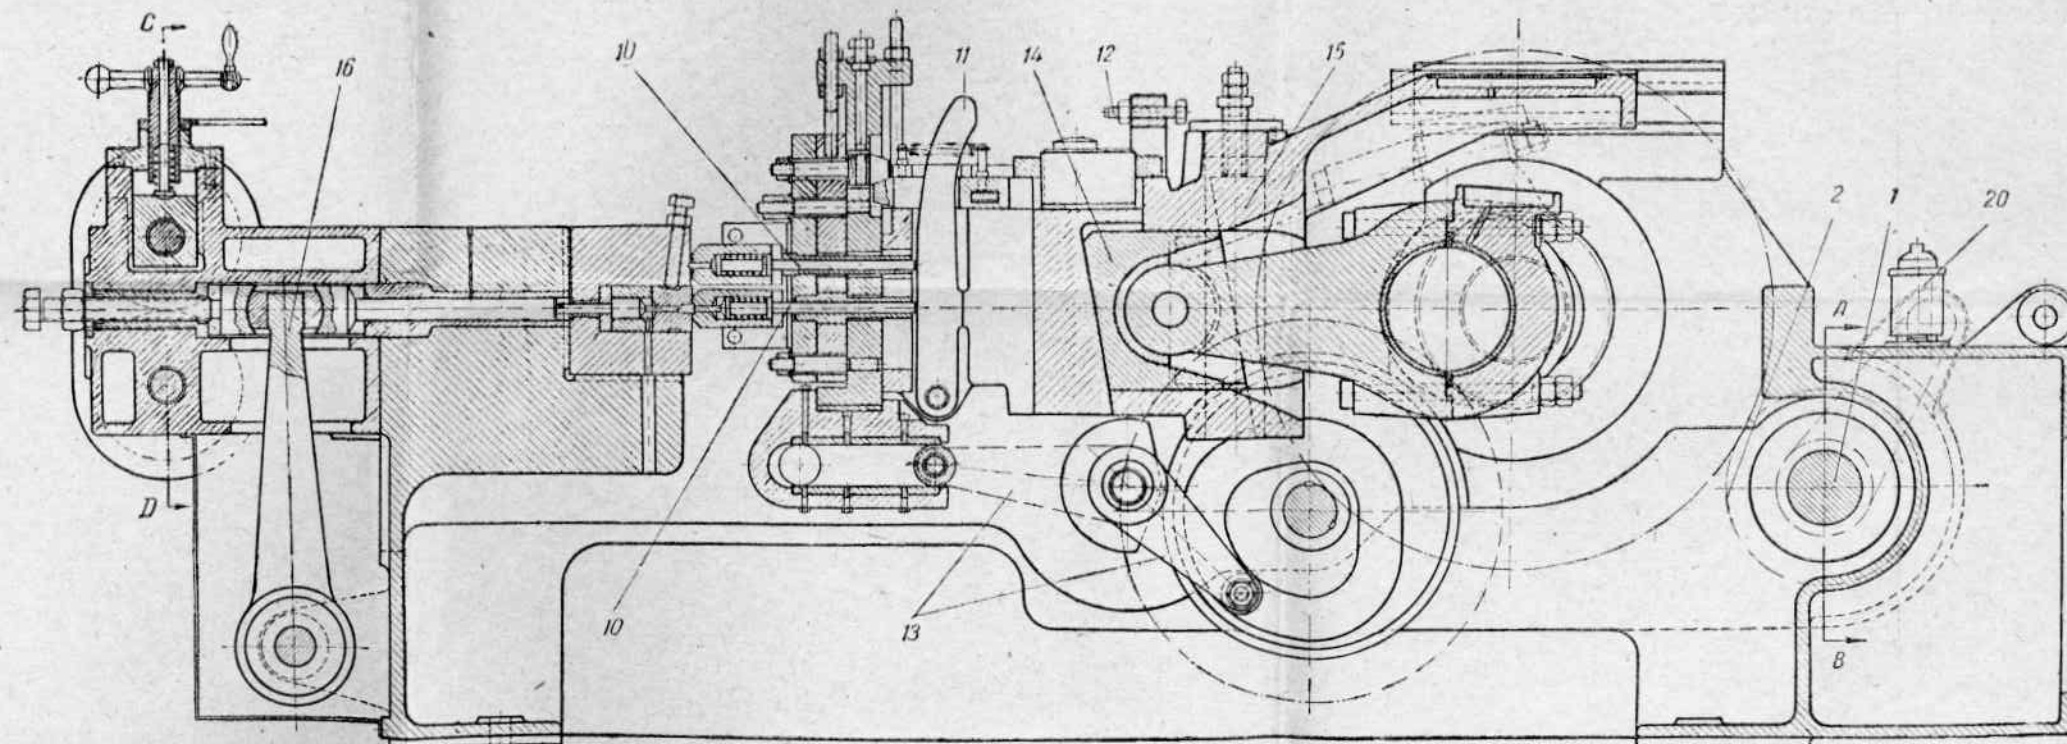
а. Двухударный холодновысадочный автомат с цельной матрицей фирмы Кизерлинг мод. DN3-9. Вид со стороны прибора выталкивания и поперечный разрез
